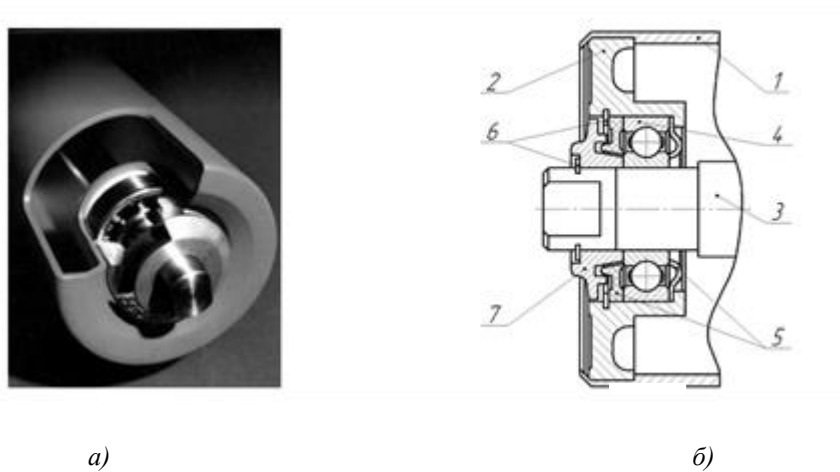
Конструкція роликового вузла: а) загальний вигляд; б) підшипниковий вузол [1, с. 17]
